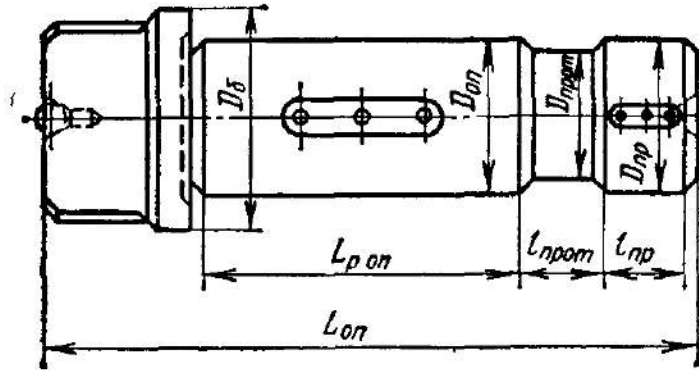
Цилиндрическая оправка для прессовой установки заготовки
